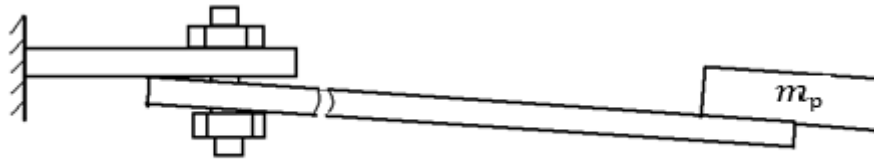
Загальний вигляд різьбового з'єднання з зазором.
